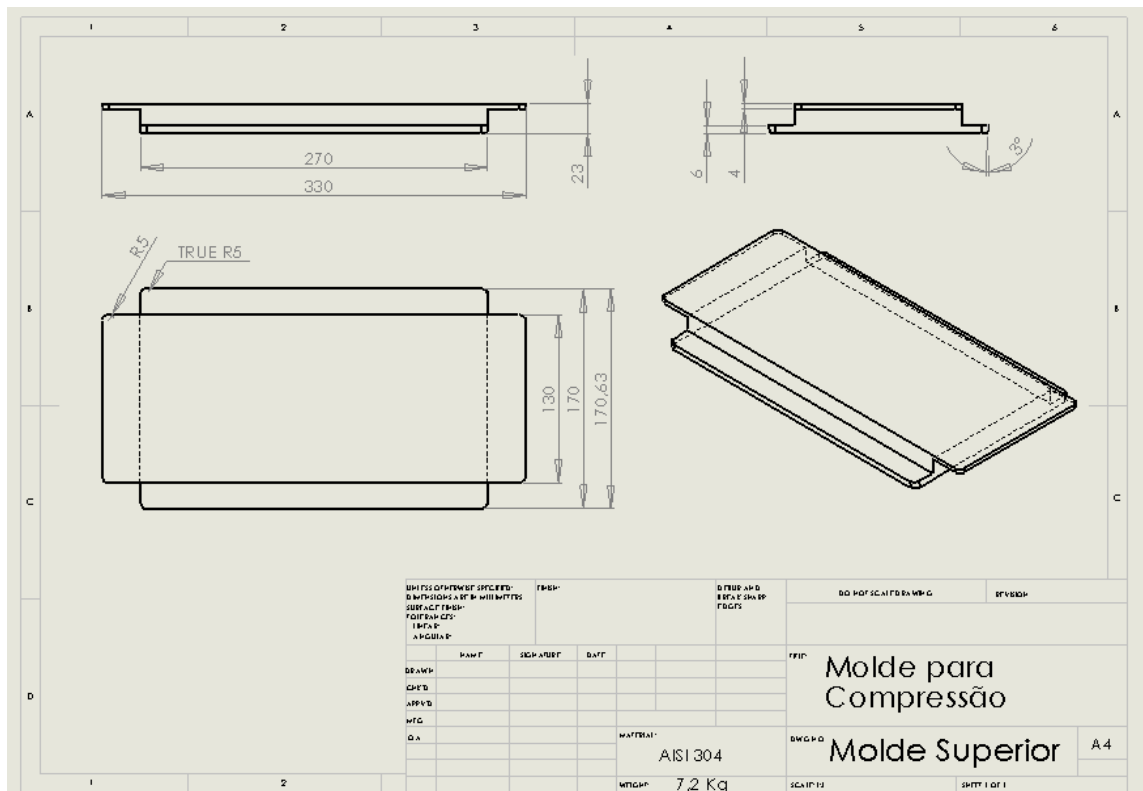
Desenho da parte superior do molde construído - Molde 2.
